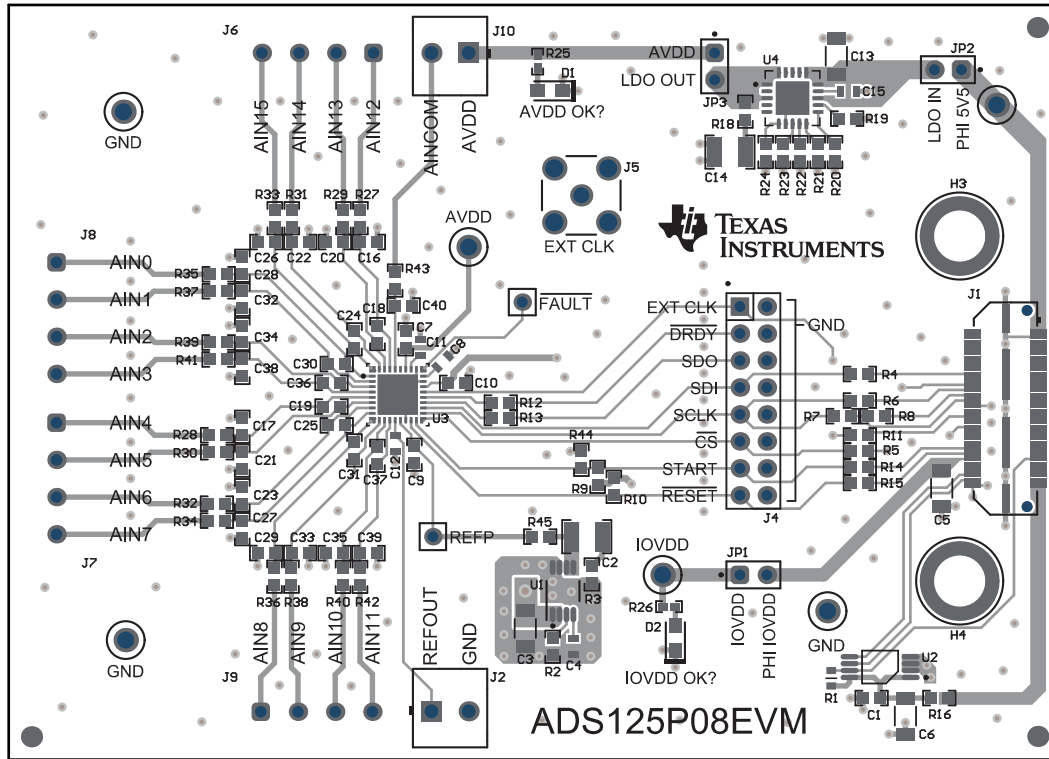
ADS125P08 評価基板 PCB レイアウト — 上面層
